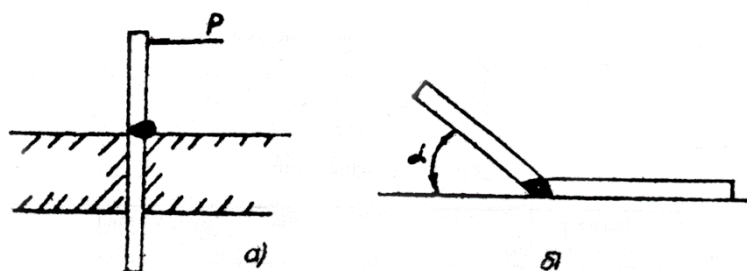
Схема испытания сварных соединений на изгиб (а) и определения угла загиба (б)
